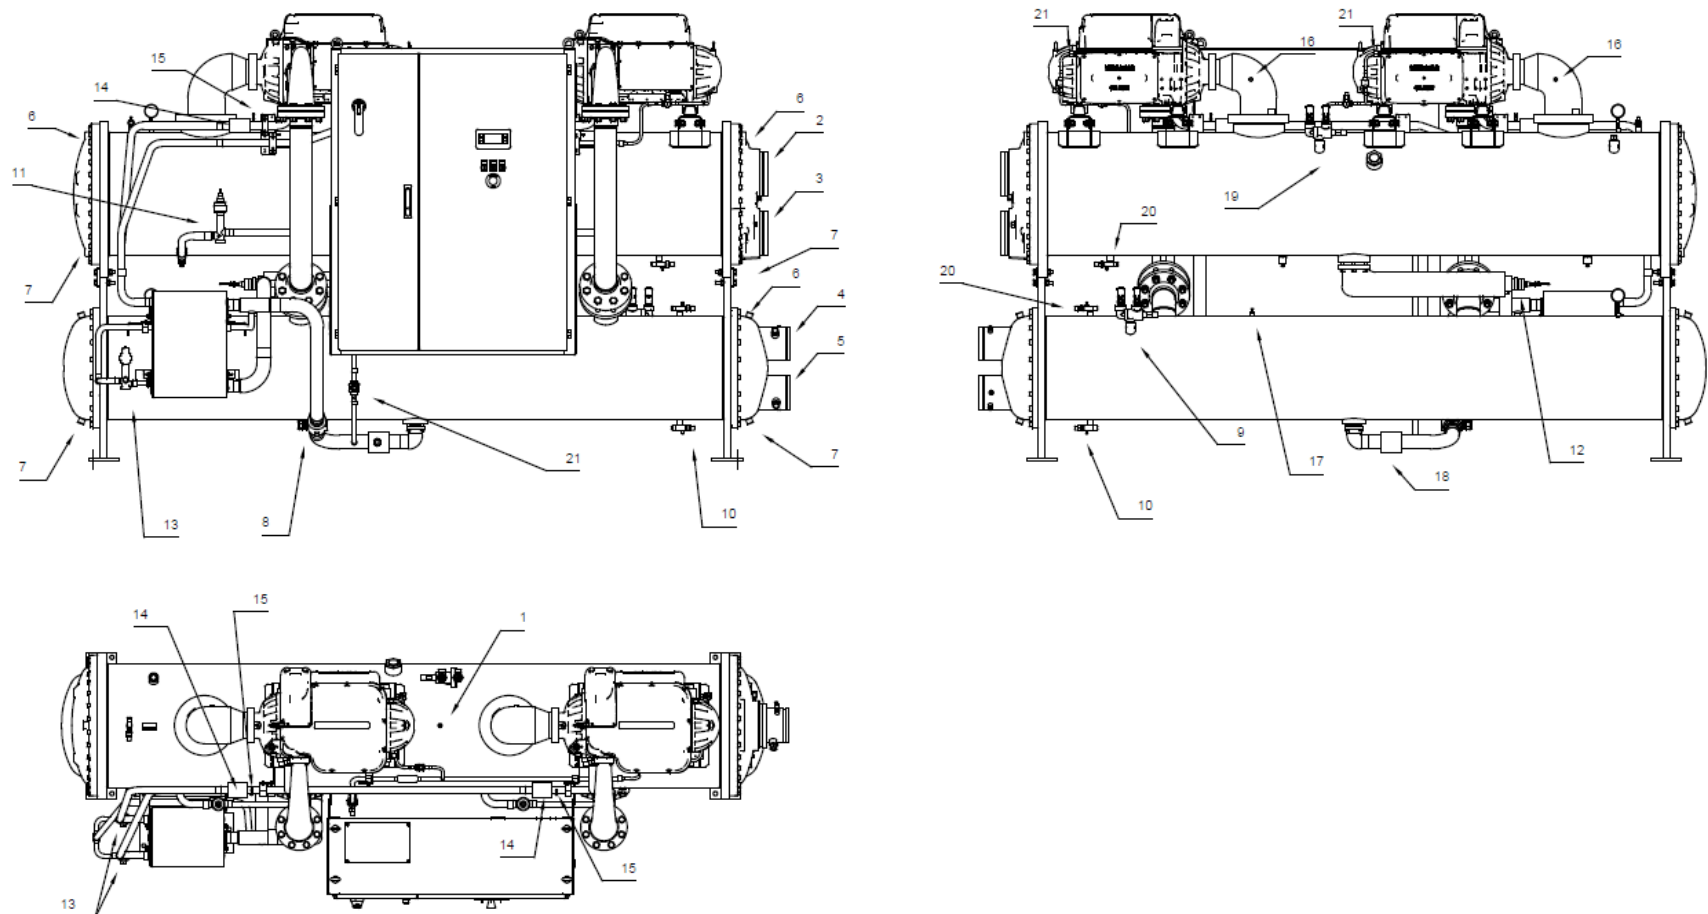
Beskrivningar av komponenter för dubbel kompressorenhet
